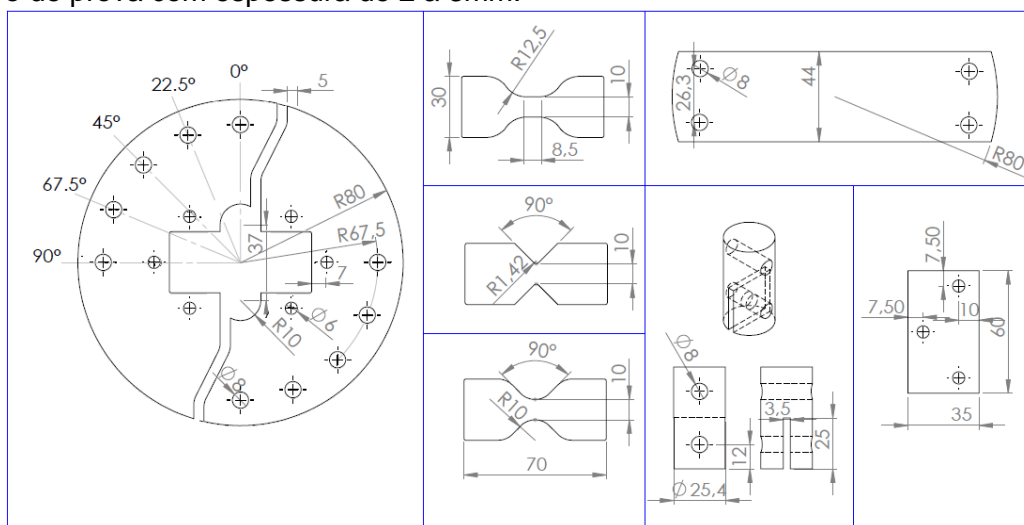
Dimensões do conjunto de ensaio [Elaborado pela autora].
